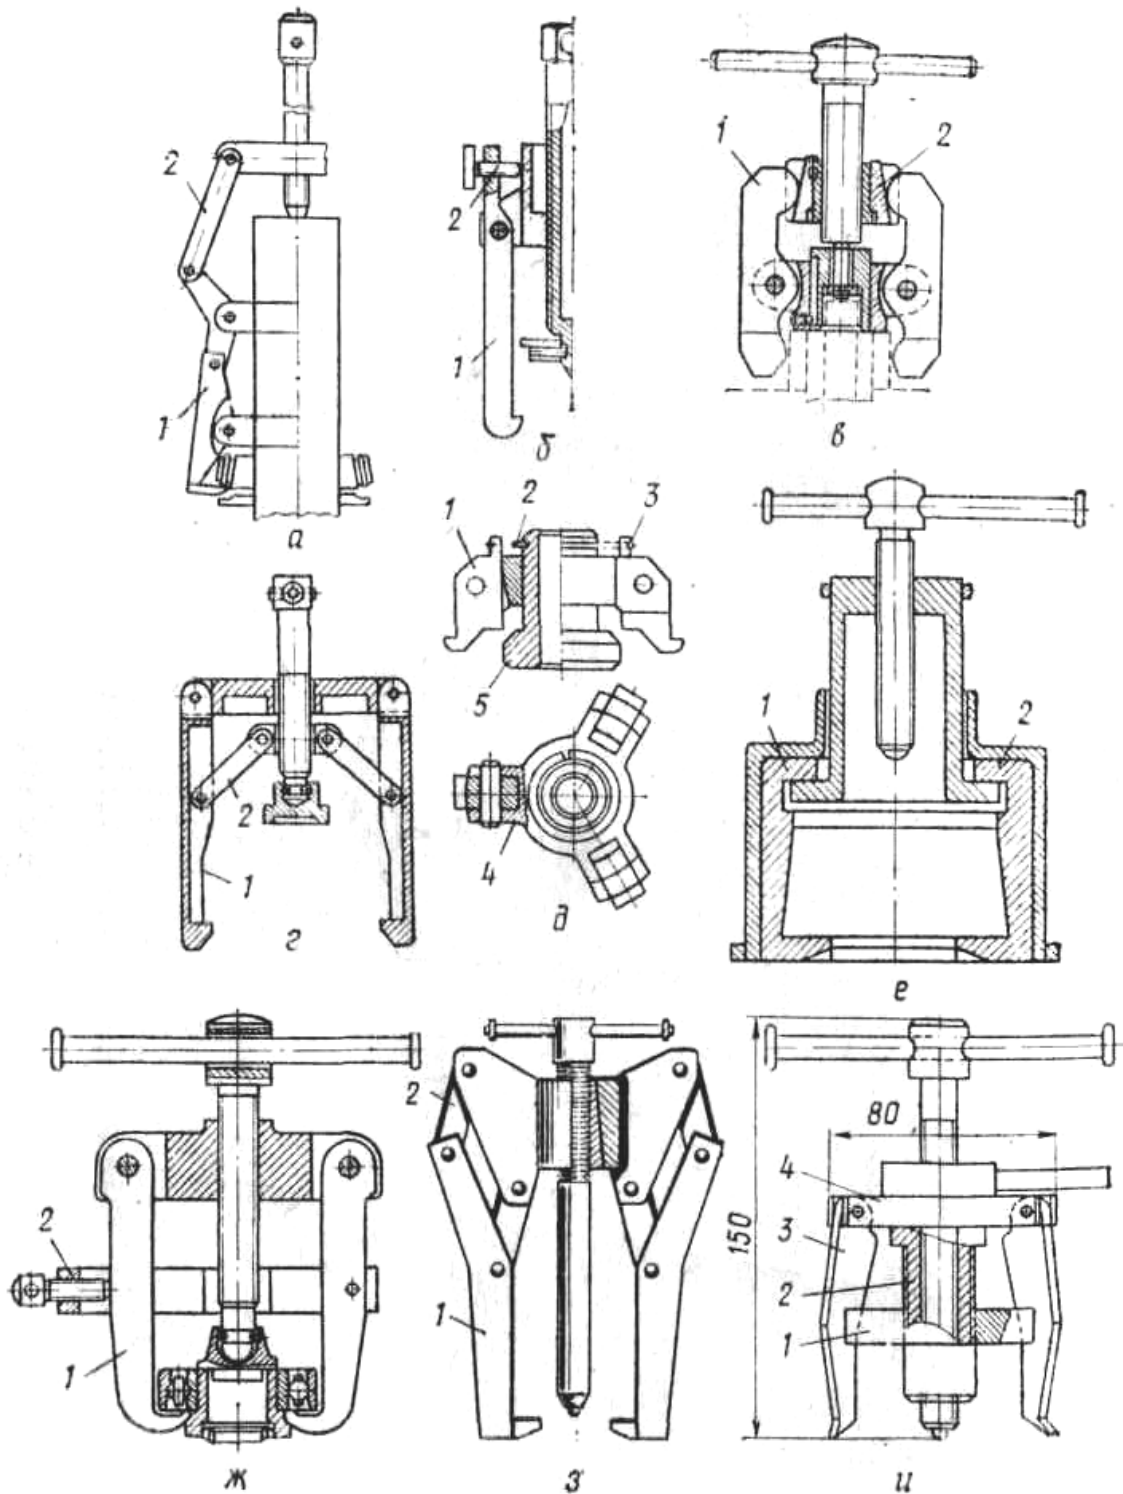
Способи притискання лапчастих захватів до деталі, яка знімається: *а, г, з* – системою тяг: 1-захвати, 2-тяги, *б* – гвинтом: 1-захват, 2-гвинт; *в* – конусом: 1-захват, 2-конус; *д* – пружиною: 1-захват, 2-запірне кільце, 3-пружина, 4-хрестовина, 5-втулка; *е* – обоймою: 1-обойма, 2-захват; *ж* - хомутом: 1-захват, 2-хомут; *и* – диском: 1-диск, 2-гвинт, 3-захват, 4-хрестовина.
